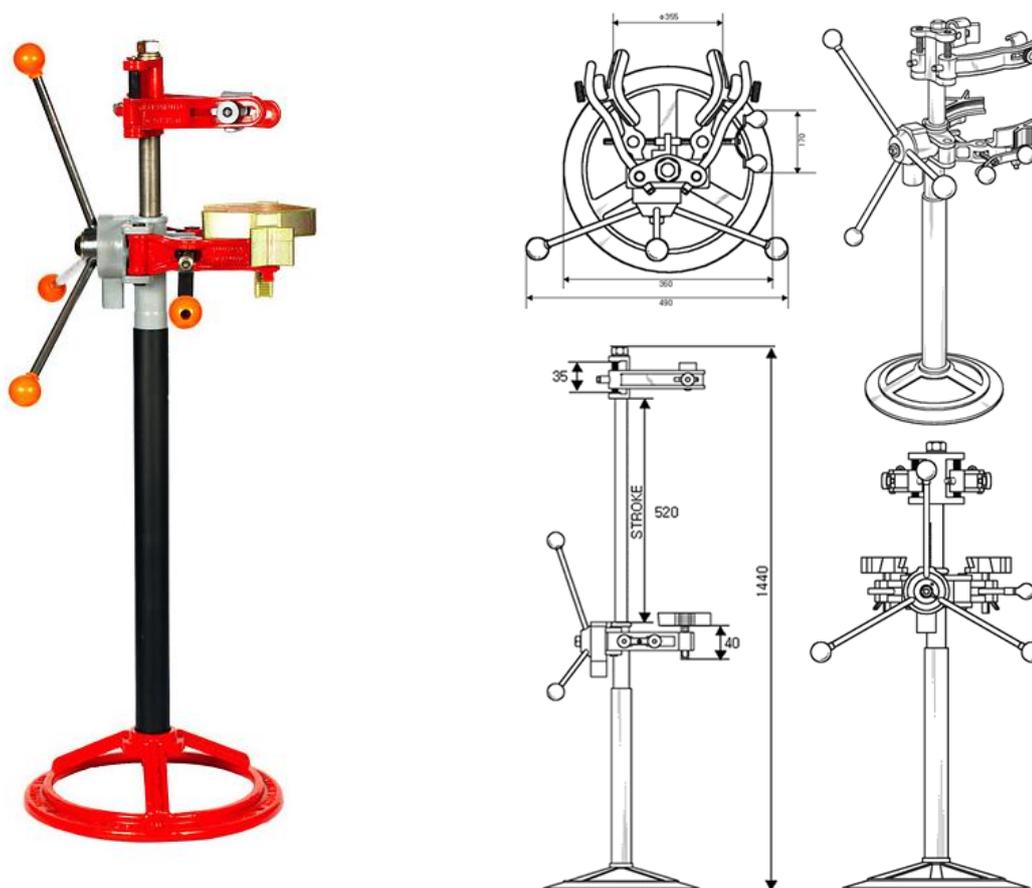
Приспособление для сборки и разборки амортизаторной стойки JackTech SK-3000
